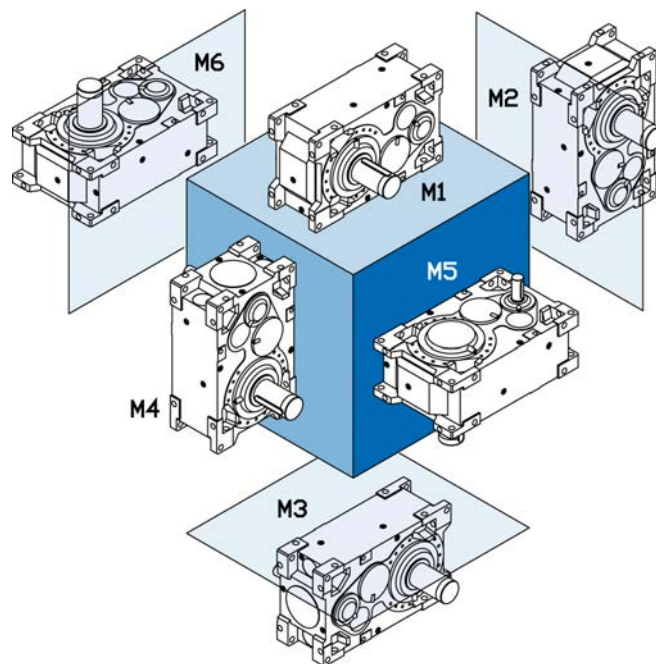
Einbaulagen Stirnradgetriebe mit Standardmontagefläche
